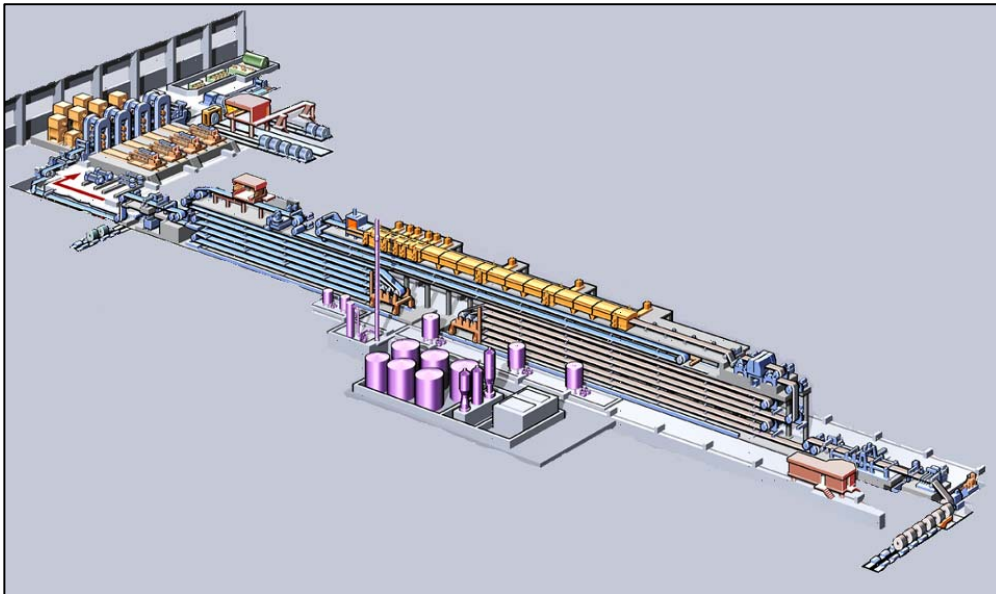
Layout da Linha de Decapagem e Laminação a Frio (PLTCM).⁽⁶⁾
